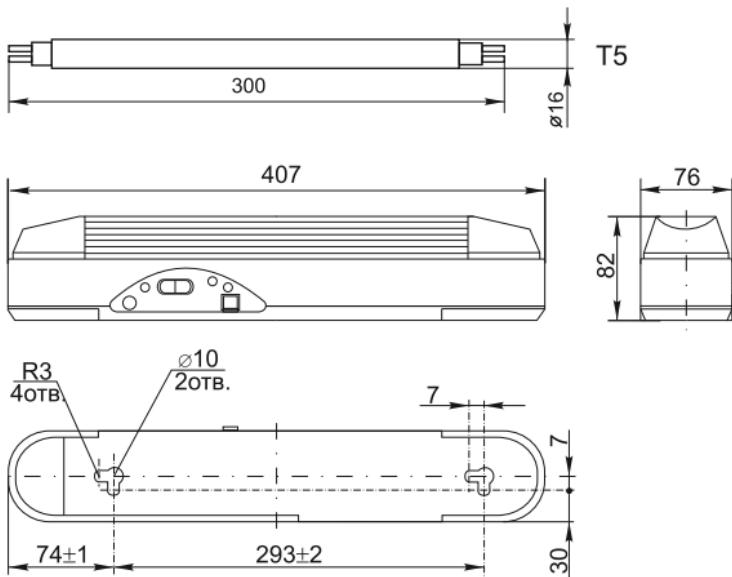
Габаритные размеры светильников ЛБА 3923, ЛБА 3923А
